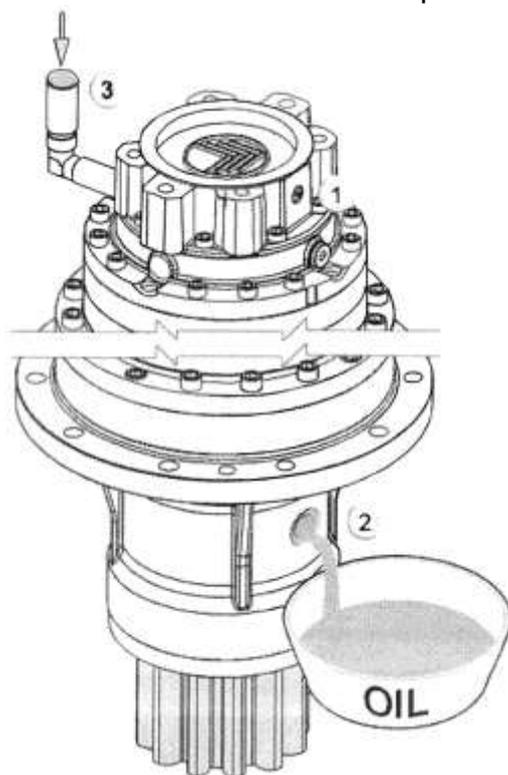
Схема залива и слива масла из редуктора механизма поворота, контроля уровня масла
